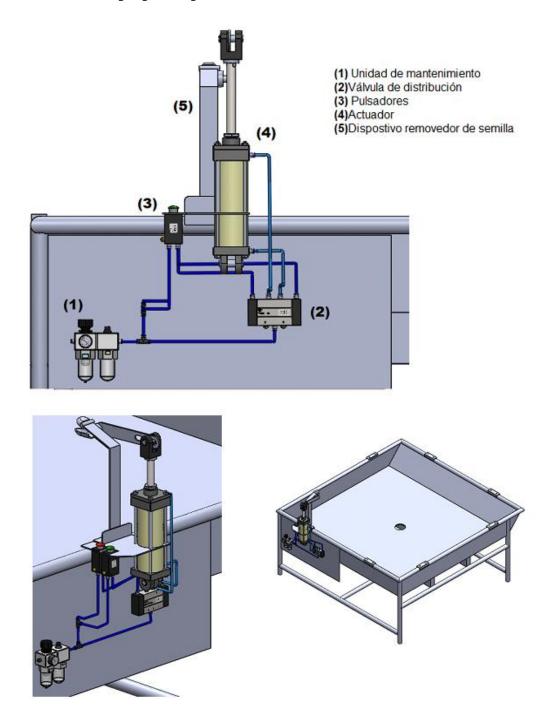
Ensamble del diseño neumático propuesto para la remoción de la semilla de durazno, con sus partes y algunas vistas importantes. (Fuente: Autor).
